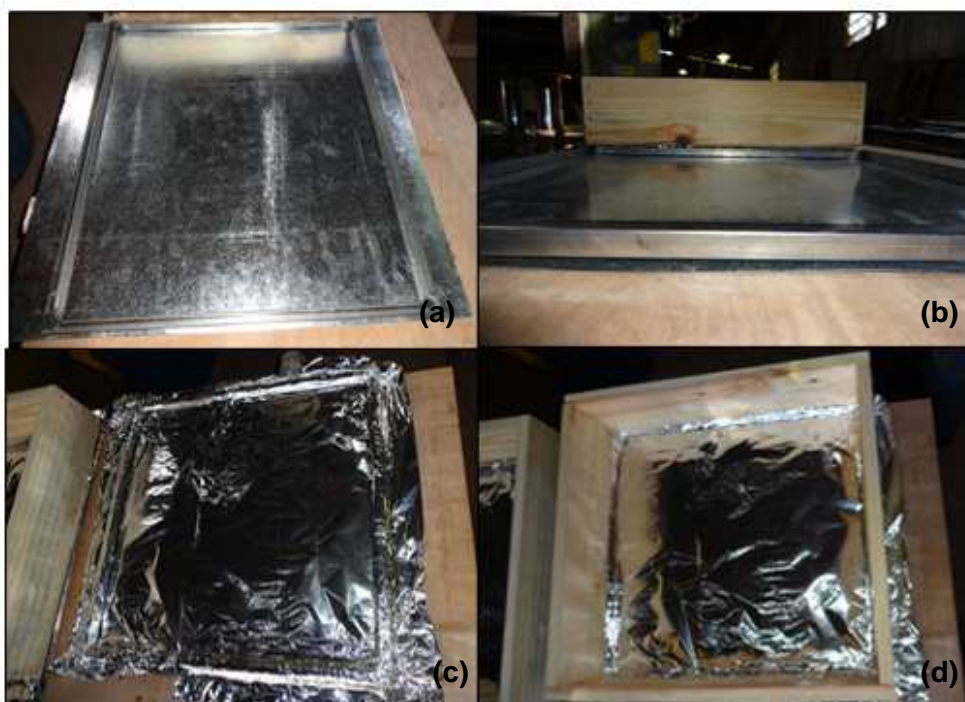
a) Molde de metal; b) Espessura do molde de metal; c) Papel alumínio sobre o molde de metal; e d) Molde de madeira.
